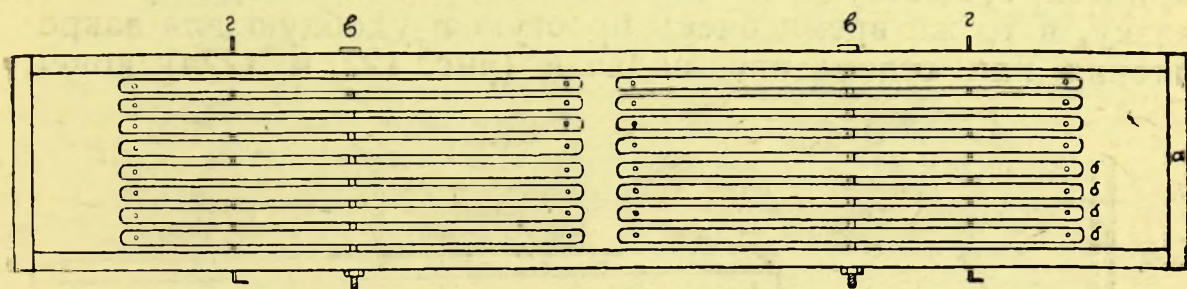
Каретка с двумя рядами журавликов — вид сверху.
